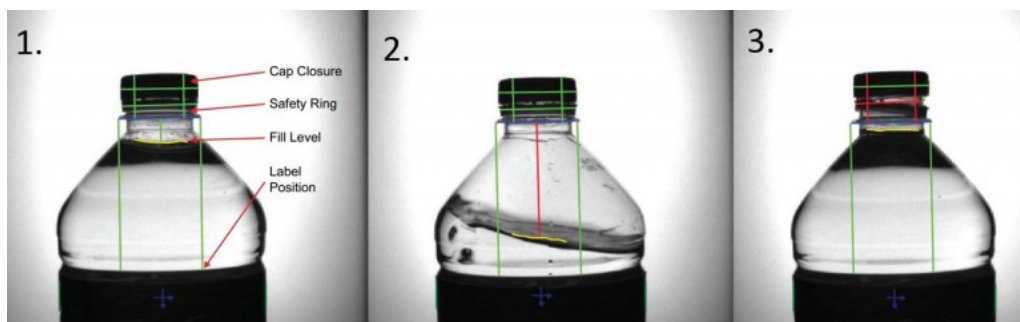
Princíp triedenia produktov pomocou kamerového systému [9].
